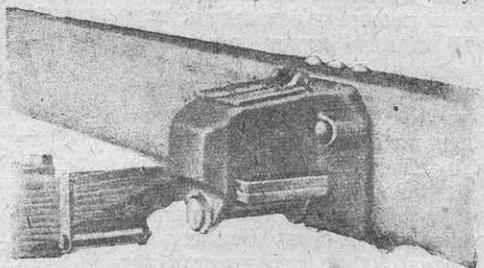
Крепление скользящей рессоры в смазываемом кронштейне.
